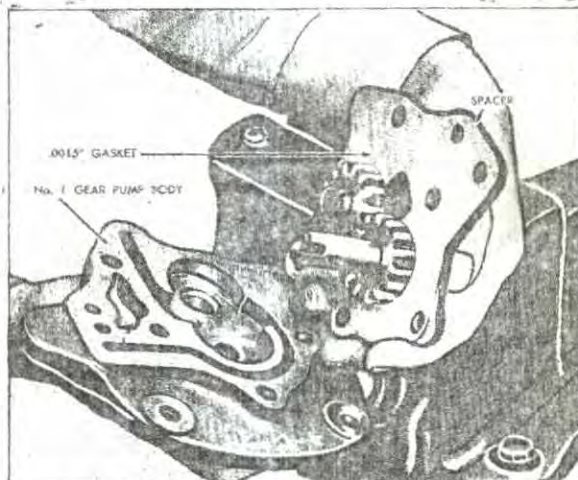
Montaje de los engranajes y cuerpo de la bomba Nº.1.
